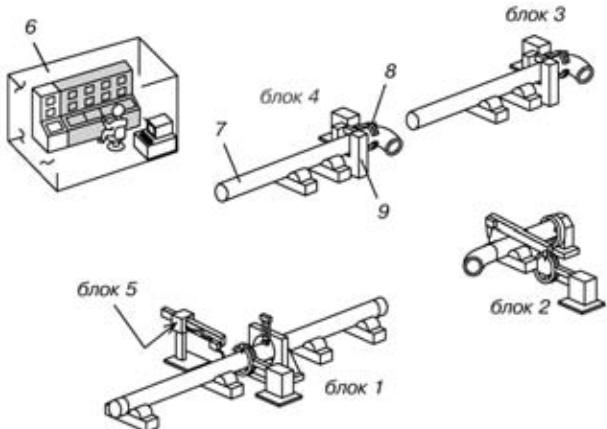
Схемы элементов сварочной установки с несколькими головками: 1–5 – подсистемы; 6 – комната оператора; 7 – труба; 8 – сварочная головка; 9 – зажимное приспособление
